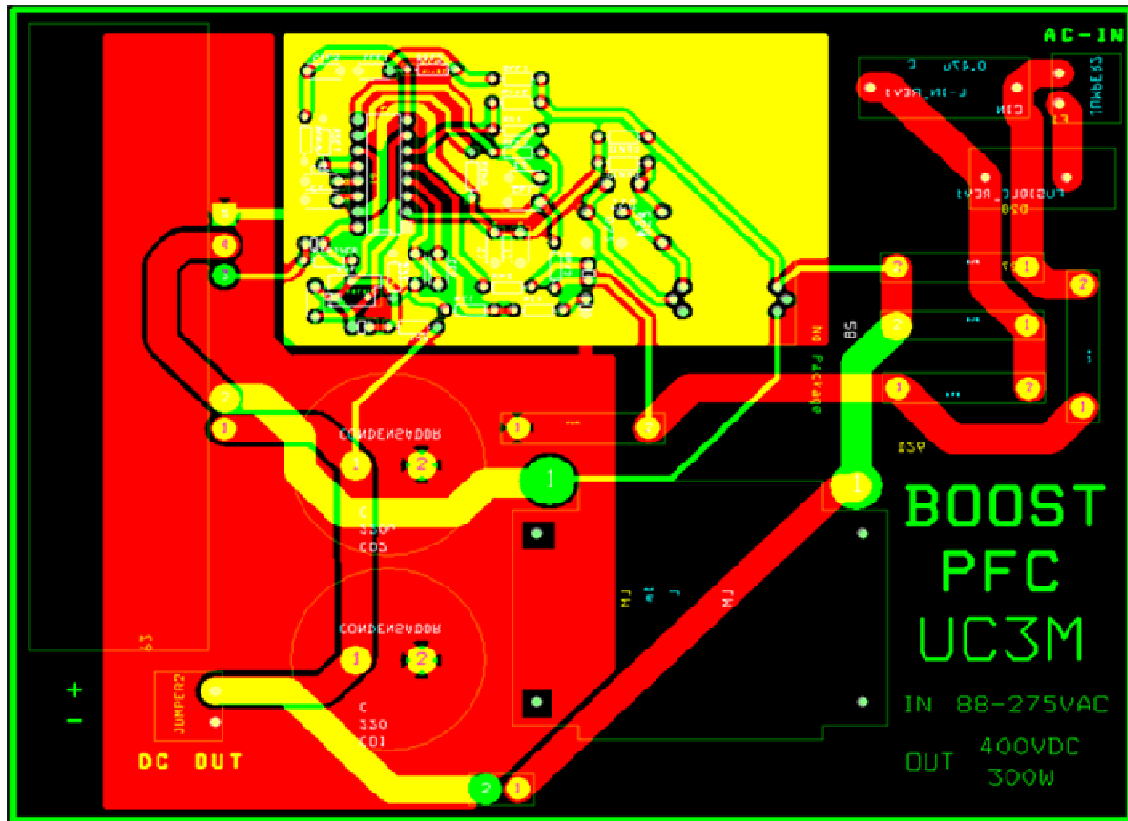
Diseño final de la PCB del Corrector de Factor de Potencia para un Elevador mediante el programa Orcad® Layout
